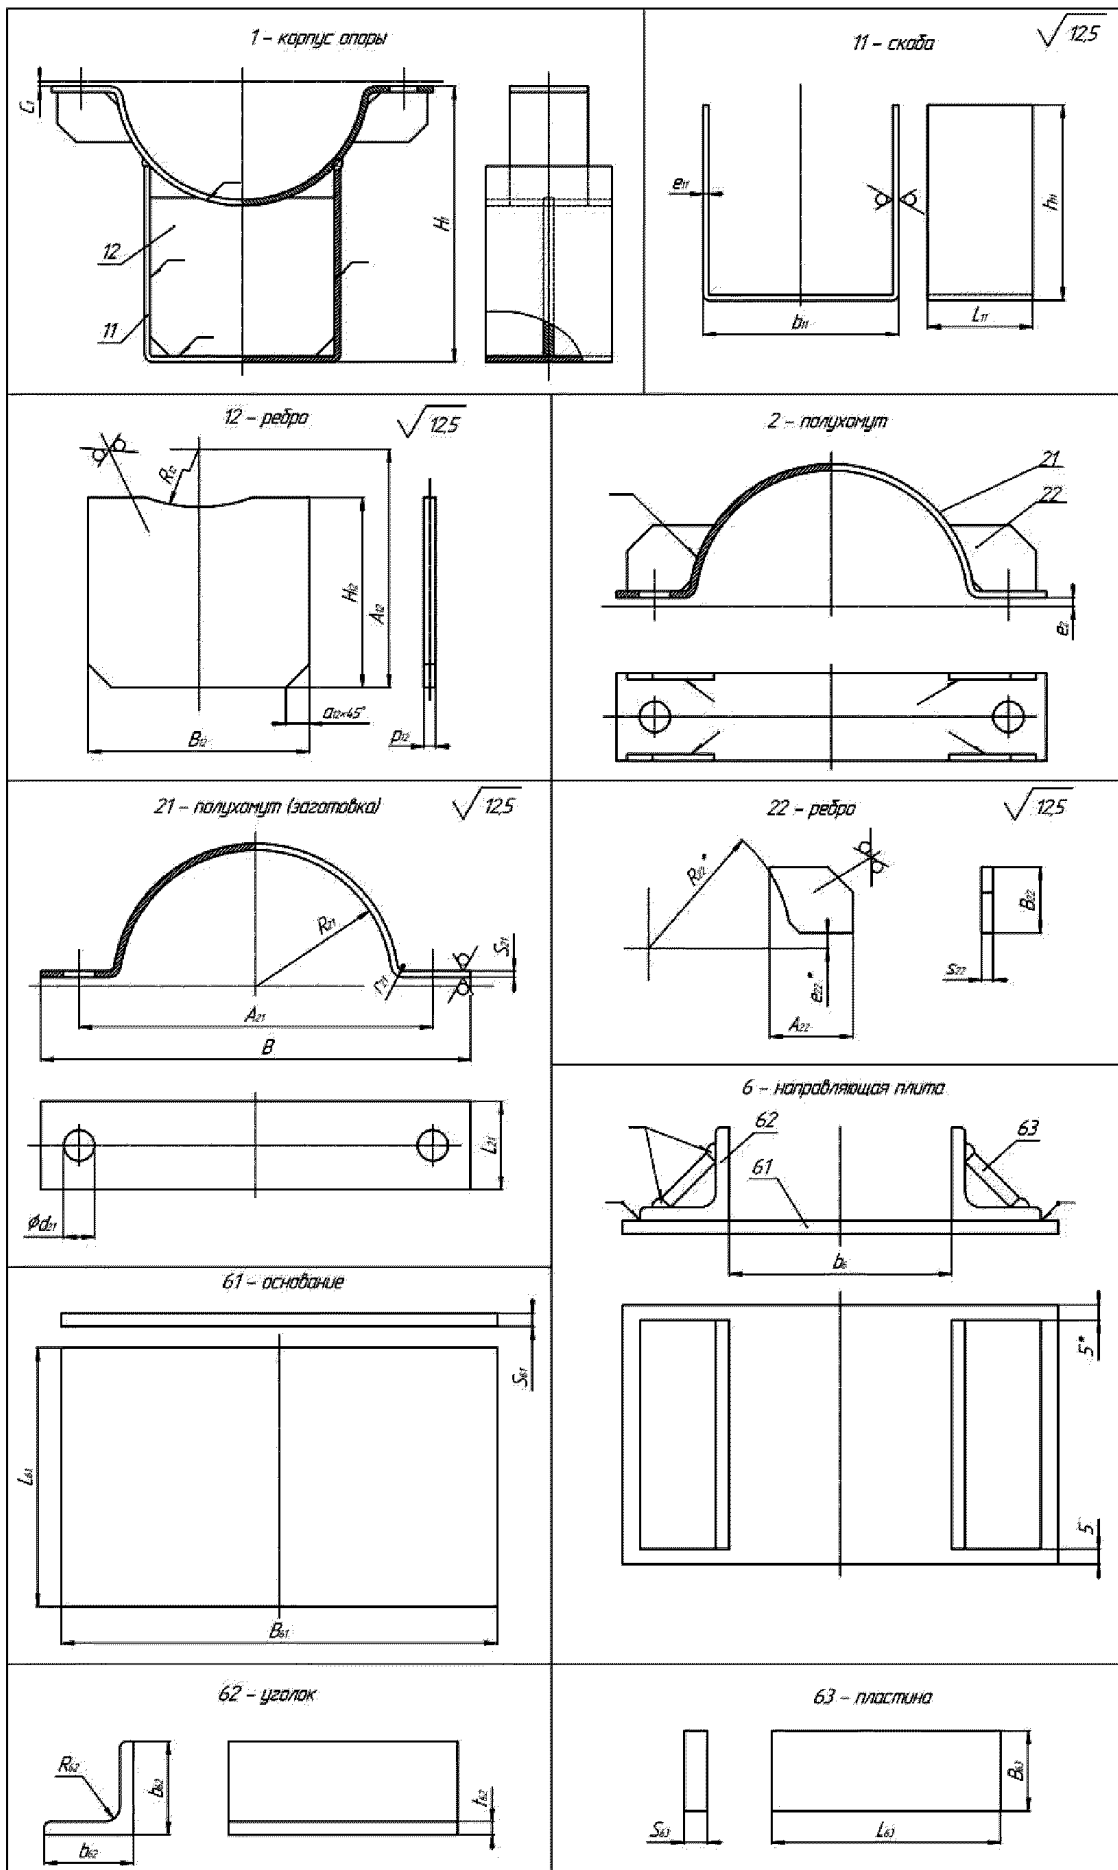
Детали изделий 01-XXXX-G-1C-03-A,
